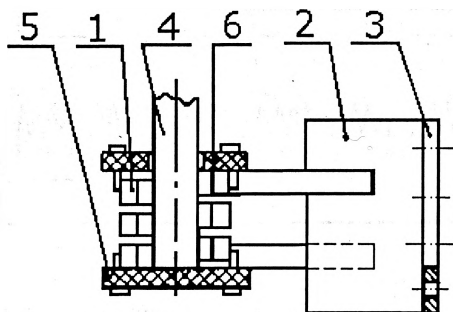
Типовой индуктор для нагрева заготовок под выдавливание. 1 — индукционная катушка, 2 — токоподводящие шины, 3 — колодки крепления к трансформатору, 4 — нагреваемая заготовка, 5 — нижняя плита, 6 — верхнее центрирующее кольцо
